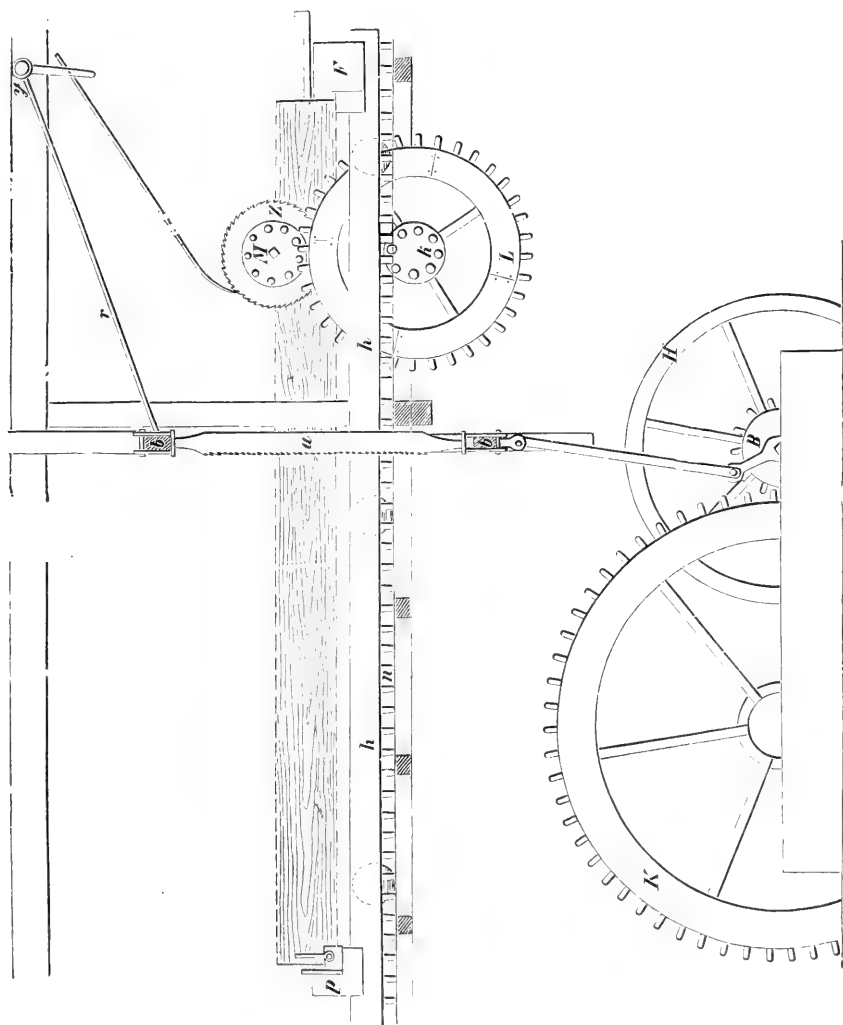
Konstruktion einer einfachen Säge mit Wasserkraftbetrieb.
